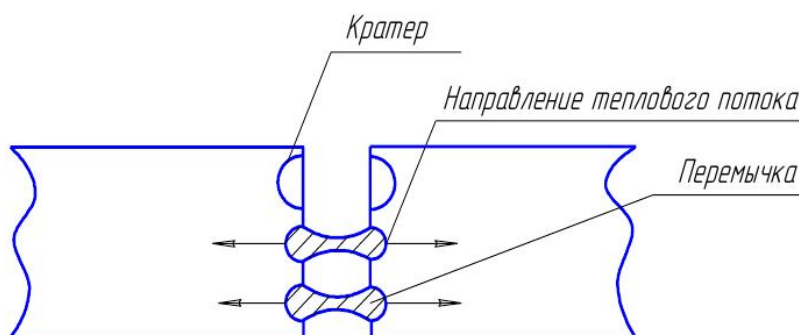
Схема расположения перемычек расплавленного металла при оплавлении
